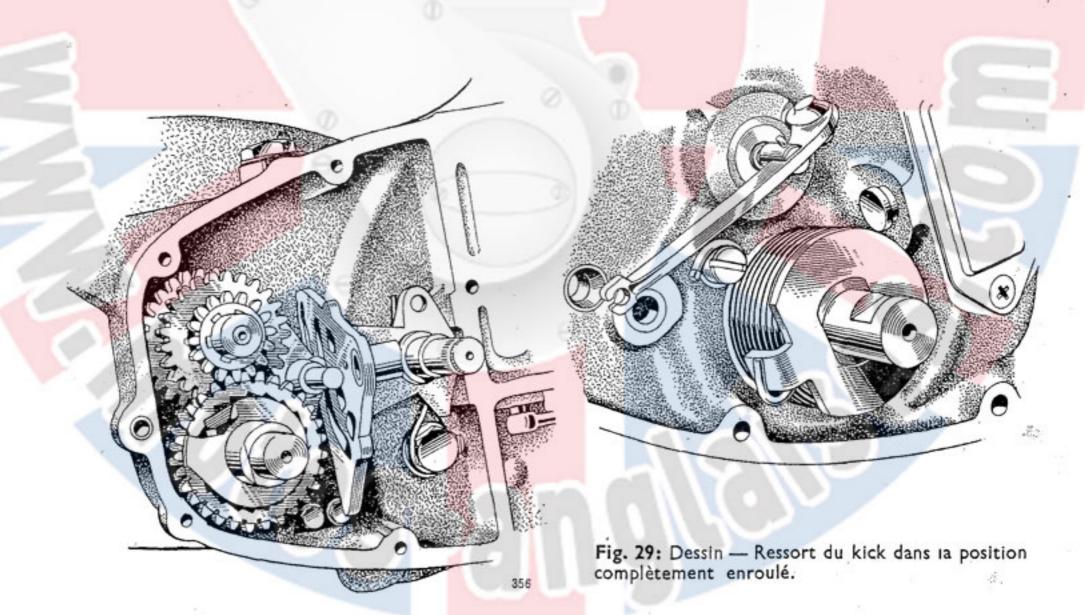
Dessin - Engrenages et mécanisme du sélecteur en place.
